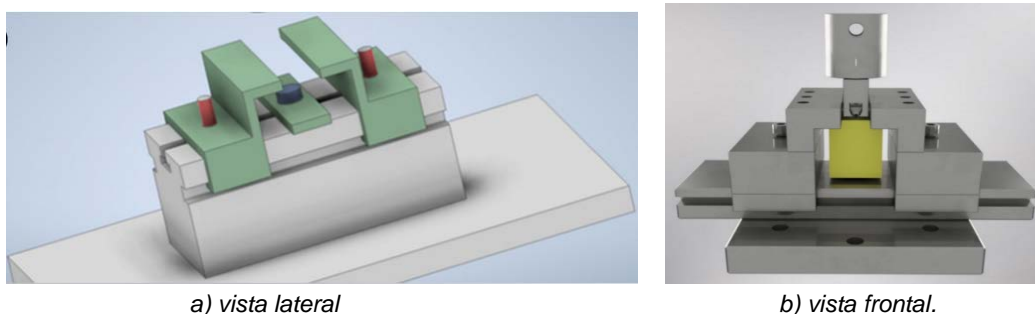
Ensamble entre la base del utillaje y el marco de la máquina universal.
